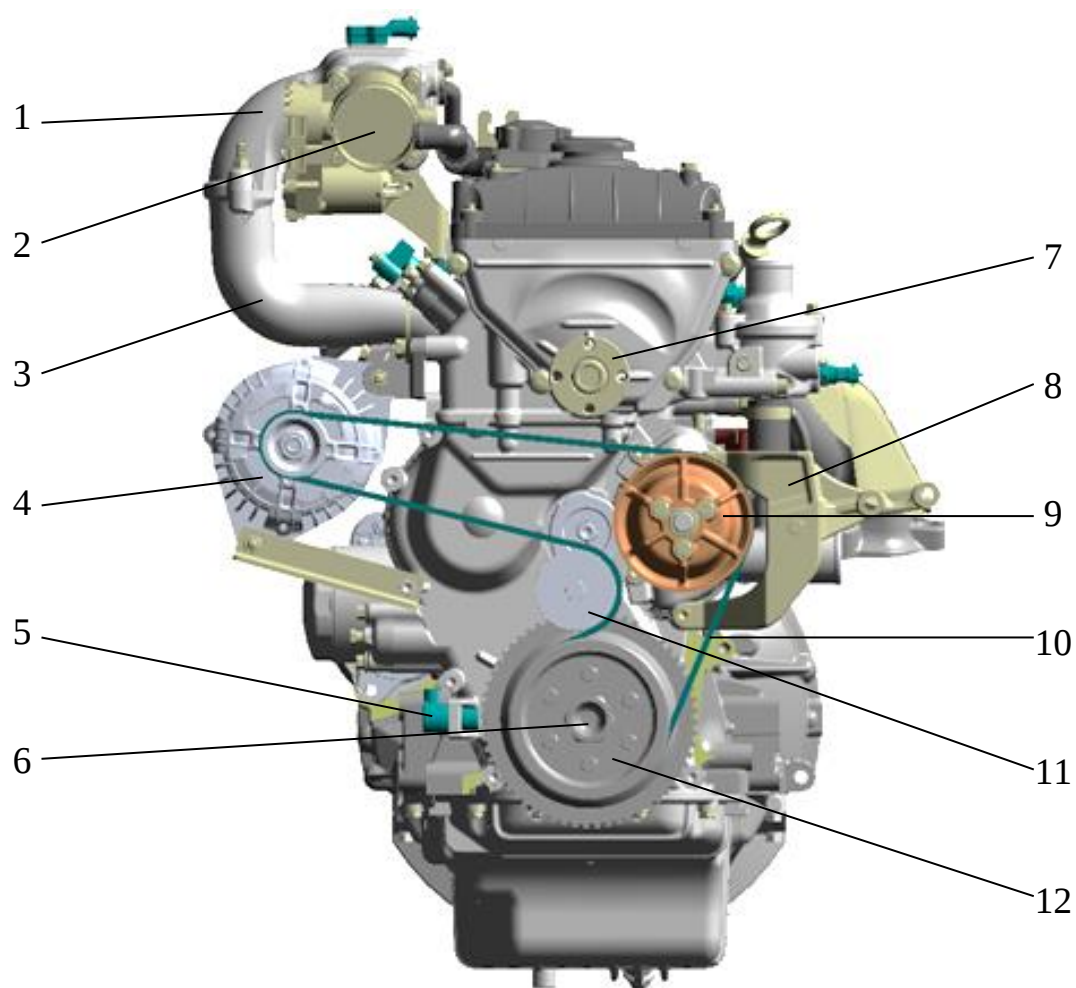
Вид двигателя ЗМЗ-409051.10 спереди:
